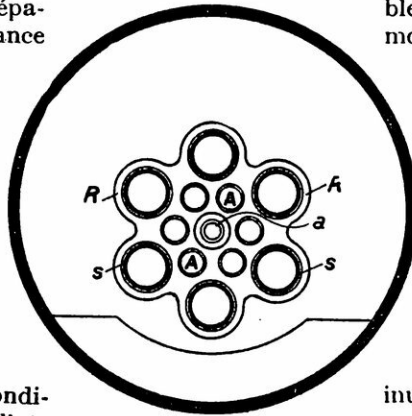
COUPE TRANSVERSALE DU MAGASIN-BARILLET
